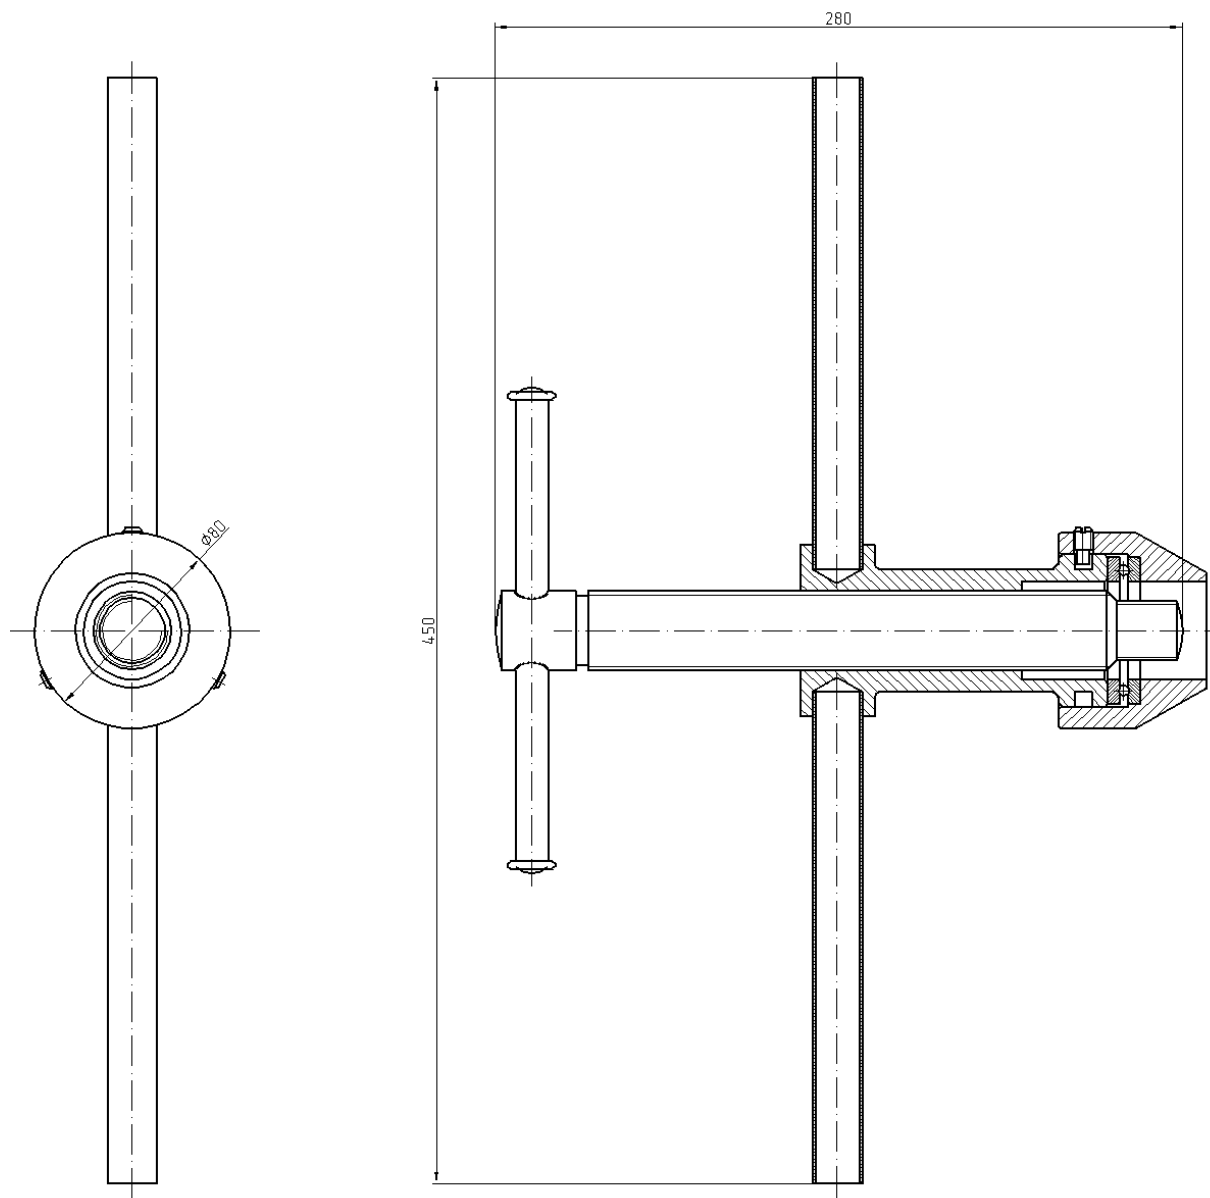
3М 7823-4291-01, Приспособление для напрессовки шестерни и ступицы на коленчатый вал
